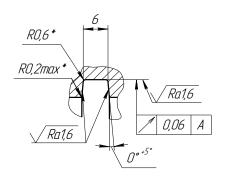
Эскиз кольцевой канавки с низкой шероховатостью
